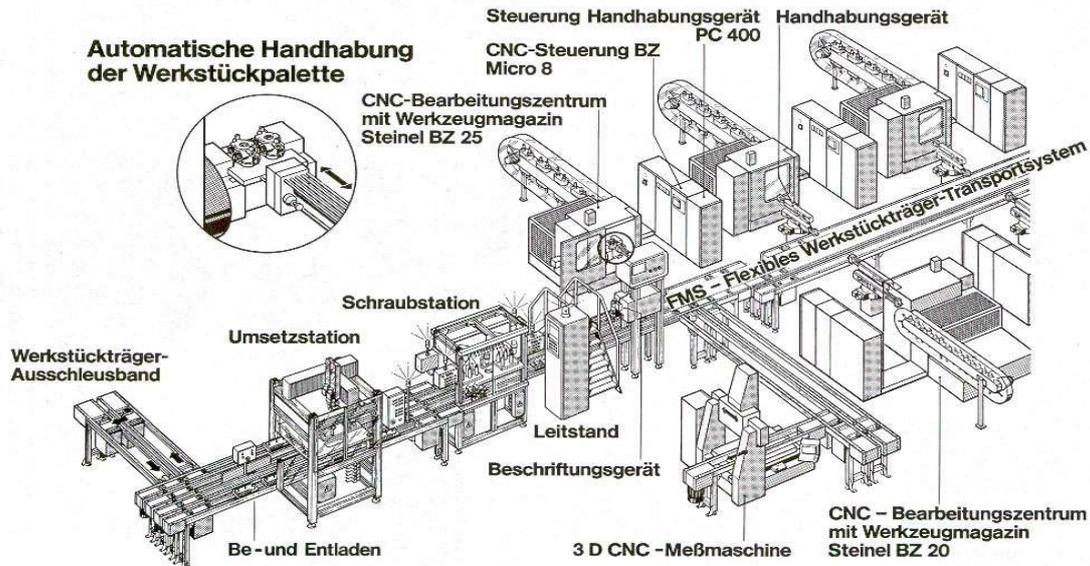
Elemente und Grundaufbau eines FFS (BOSCH Industrieausrüstung, Anwender BOSCH Stuttgart)[1]
